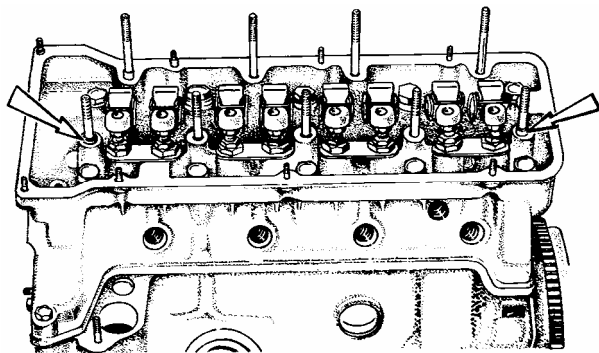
Установочные втулки для корпуса подшипников распределительного вала
